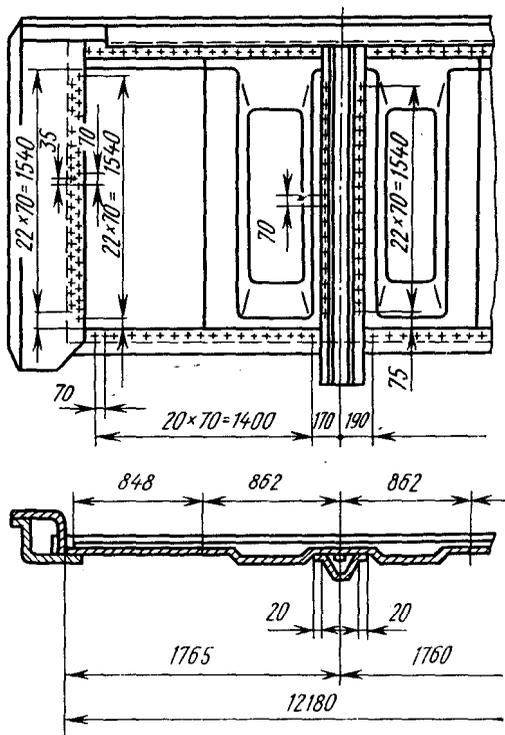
Расположение сварных точек на боковой стенке грузового полувагона
